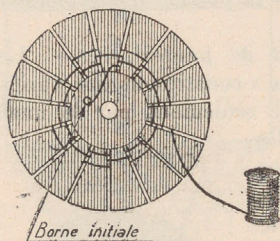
Bobinage d'un enroulement « fond de panier ».
